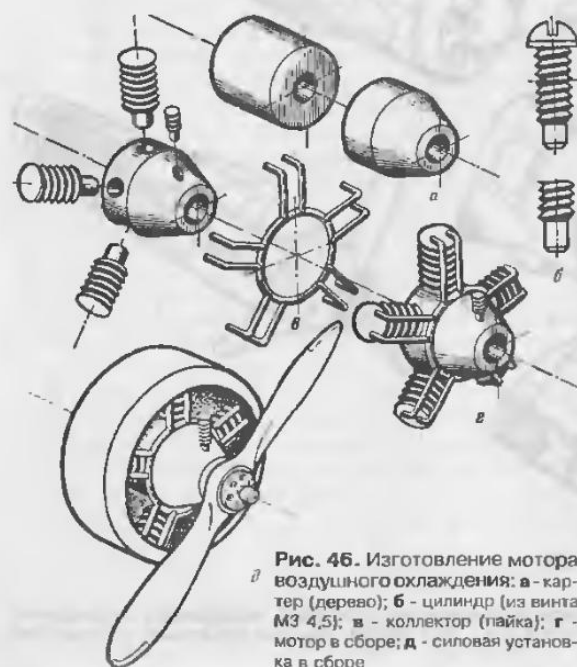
Изготовление мотора воздушного охлаждения: а - картер (дерево); б - цилиндр (из винта МЗ 4,5); в - коллектор (пайка); г - мотор в сборе; д - силовая установка в сборе
